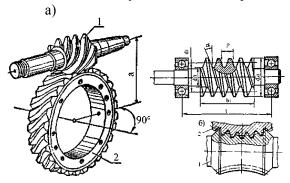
Червячная передача a — червяк с цилиндрической делительной поверхностью; e — червяк с торовой делительной поверхностью.
